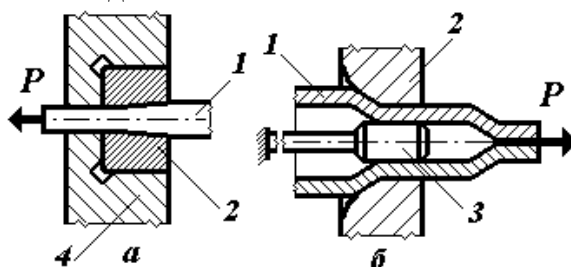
Схемы волочения: а – волочение проволоки, прутка, сплошного профиля; б – волочение трубы на оправке; 1- заготовка; 2 – волока; 3 – оправка; 4 – обойма (бандаж); P – усилие волочения
